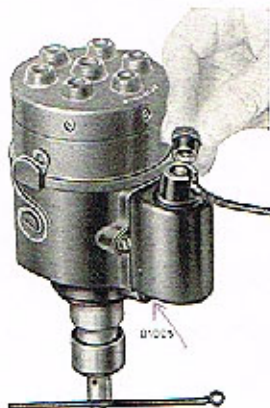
Přípojky SCINTILLA (kabelové botičky).
